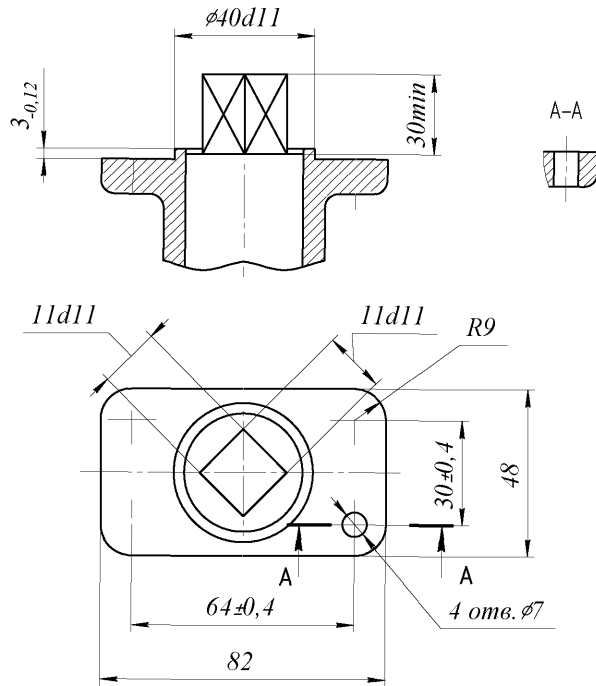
Ответное присоединение трубопроводной арматуры типа МЧ
